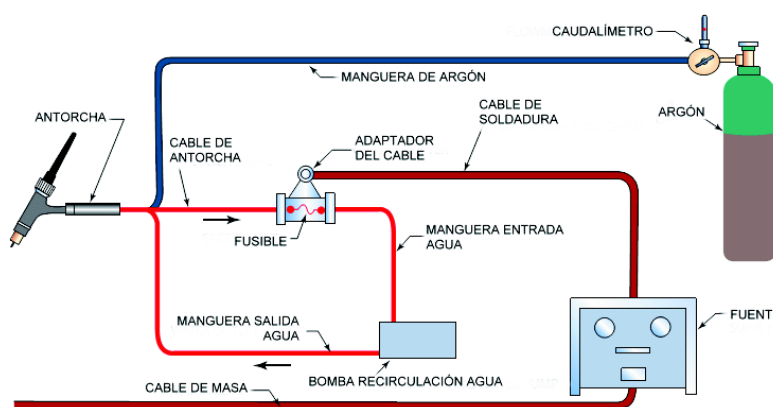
Esquema de un circuito de soldadura GTAW con pistola refrigerada por agua⁴³
